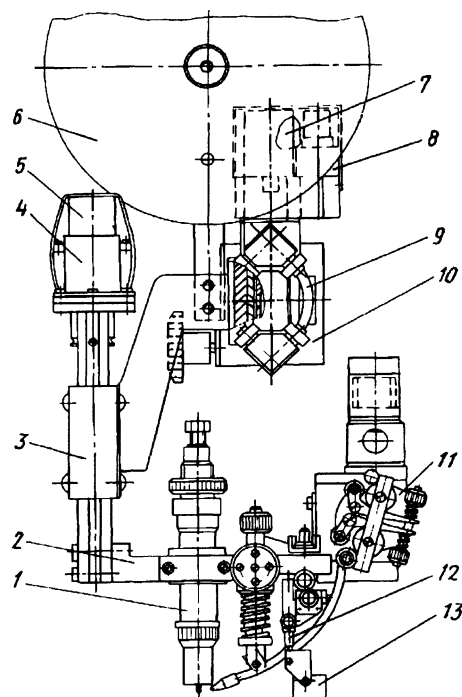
Подвесная сварочная головка АСГВ-5:
